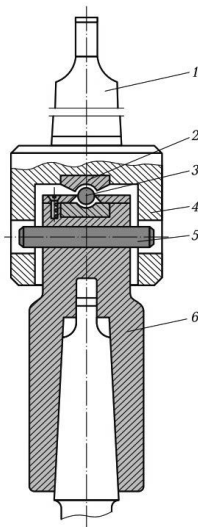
Оправка, що гойдається: 1 – хвостовик; 2 – під'ятник; 3 – кулька; 4 – корпус; 5 – штифт; 6 – коливається частина
